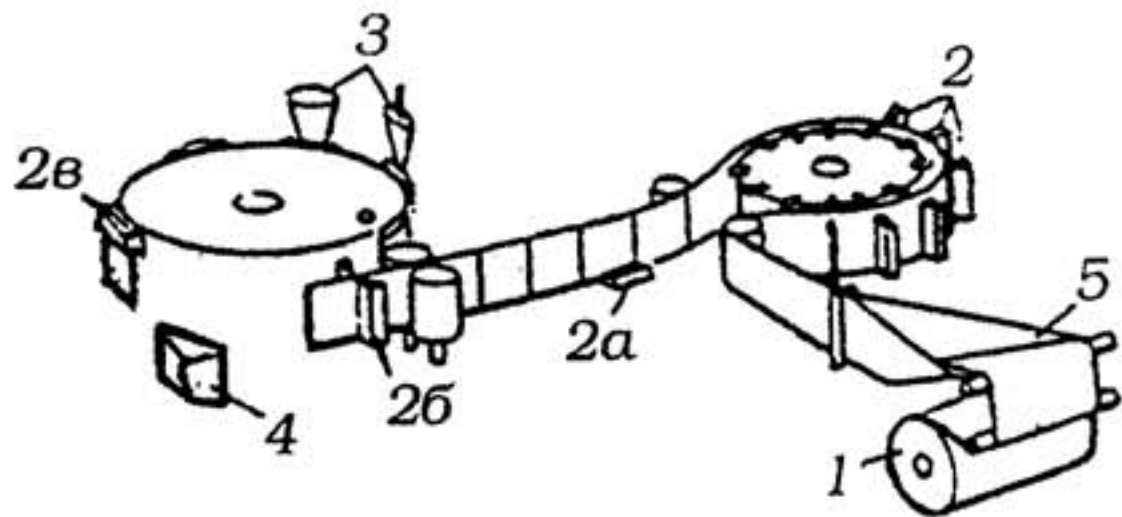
Схема горизонтального роторного способа изготовления мягкой тары: 1 — рулон пленки; 2 — сварочный ротор; 2а — нижние горизонтальные сварочные электроды; 2в — верхние горизонтальные сварочные электроды; 3 — бункеры с дозаторами; 4 — упаковка; 5 — формирующий треугольник
